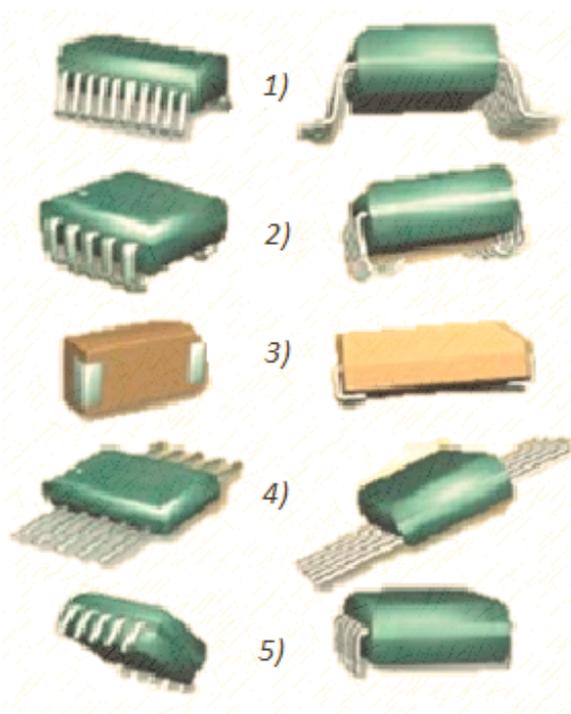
Основные типы формовки выводных ЭРЭ для поверхностного монтажа
